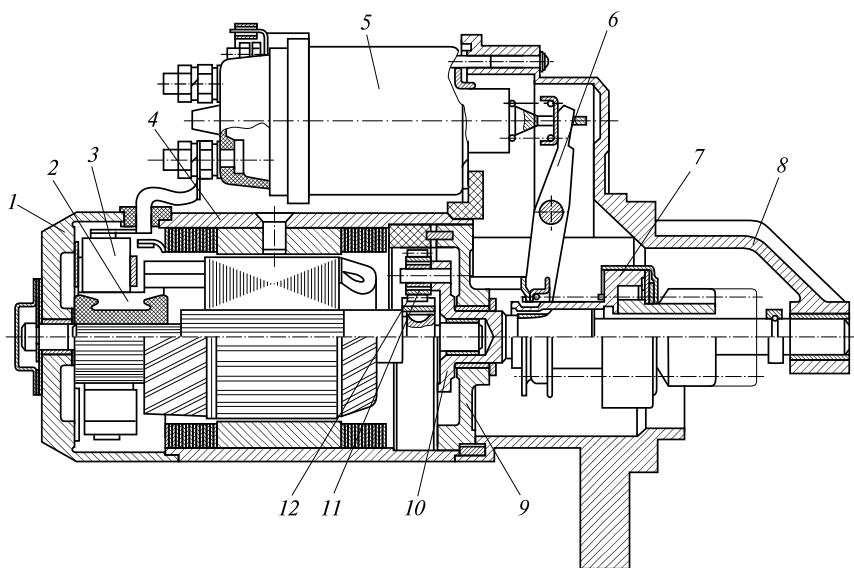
Конструкция стартера с планетарным редуктором:
